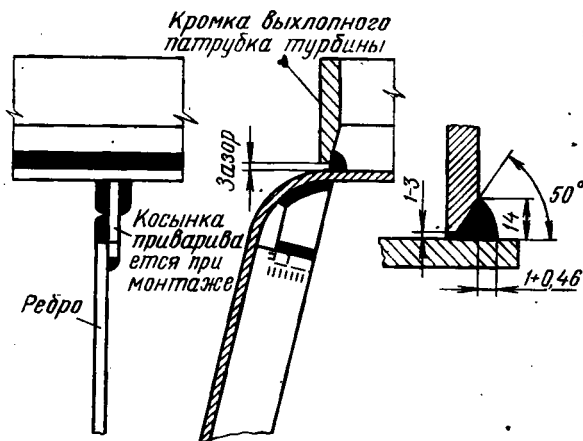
Соединение выхлопного патрубка цилиндра турбины с конденсатором посредством сварки
